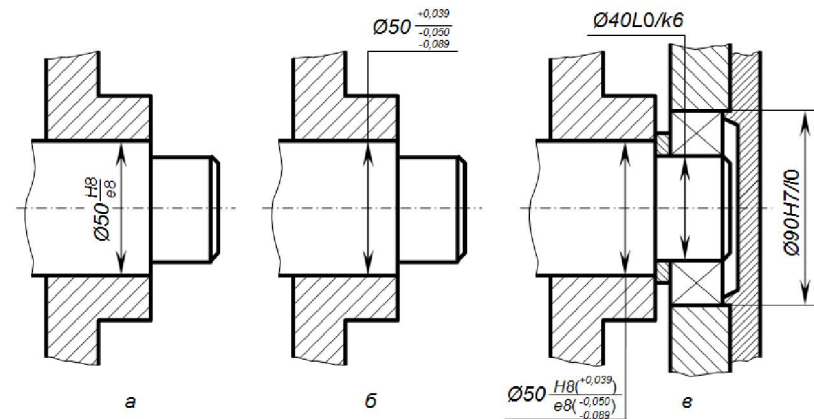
Примеры обозначения посадок на сборочных чертежах
